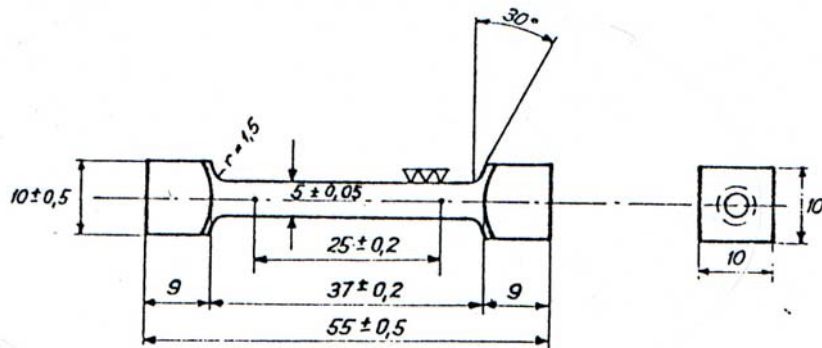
Dimensiones de la probeta Minitrac de metal de aporte puro para ensayo de tracción (168).
